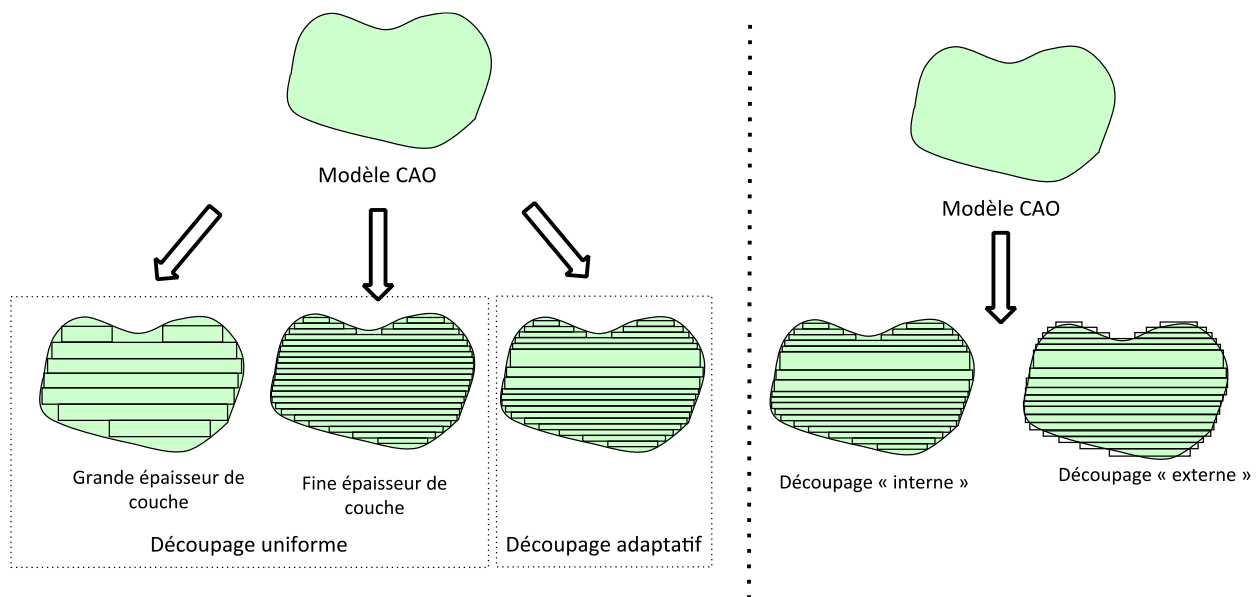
Opérations de découpe ou « slicing » uniformes ou adaptatives et internes ou externes
